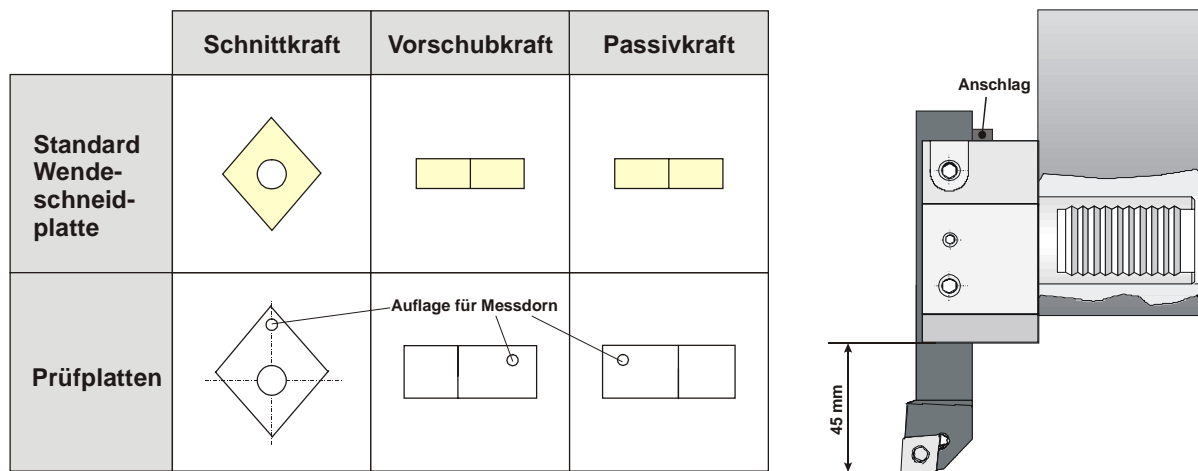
Ausrüstungselemente für Messungen in der Zugprüfmaschine
